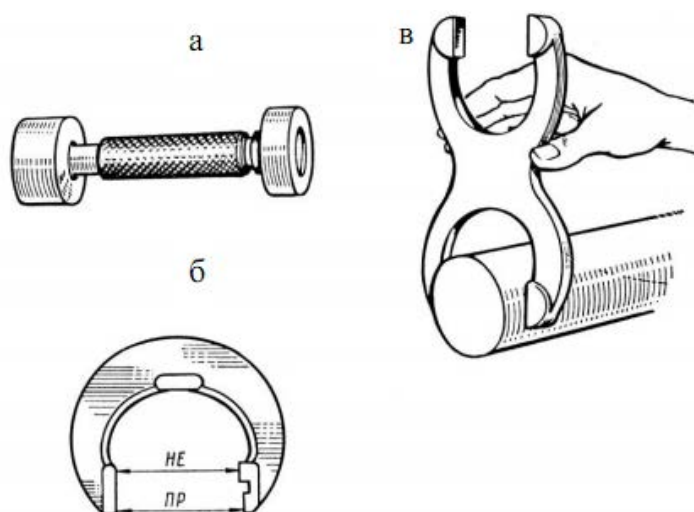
Предельные калибры: а – пробка двусторонняя, б – скоба односторонняя; в – измерение вала скобой двусторонней
